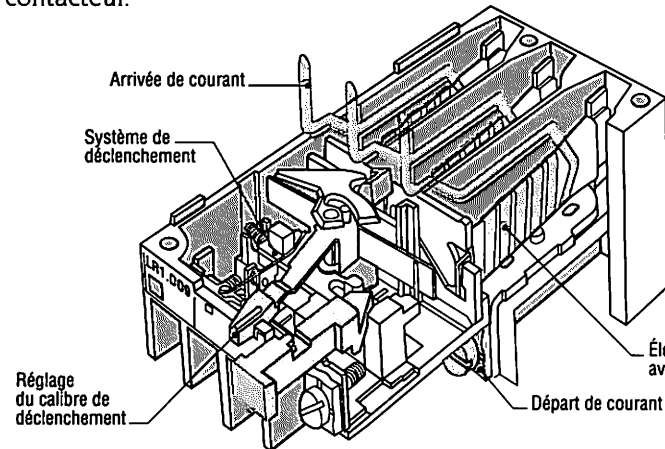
Vue éclatée d'un relais thermique (Télemécanique).
